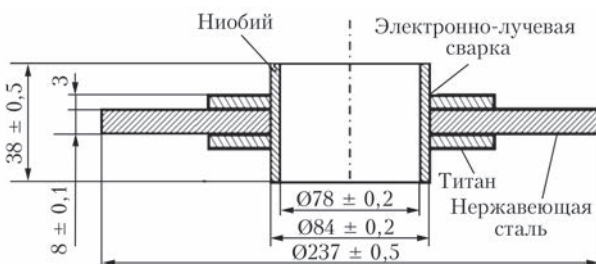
Конструкция переходника, обеспечивающая отсутствие образования при сварке интерметаллидов ниобия
